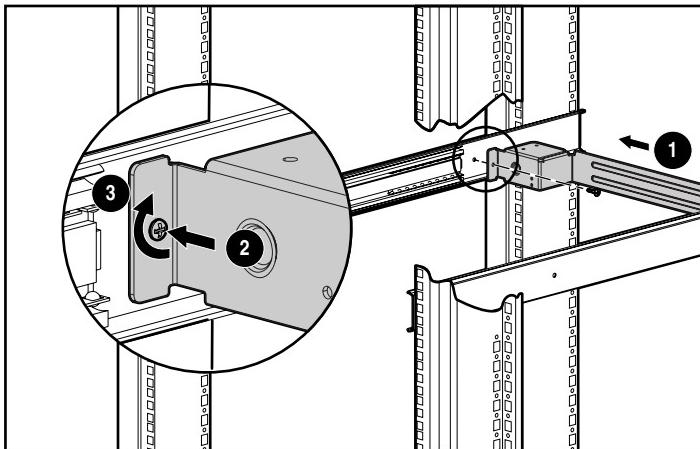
Fijación de la pieza de refuerzo al soporte de montaje
